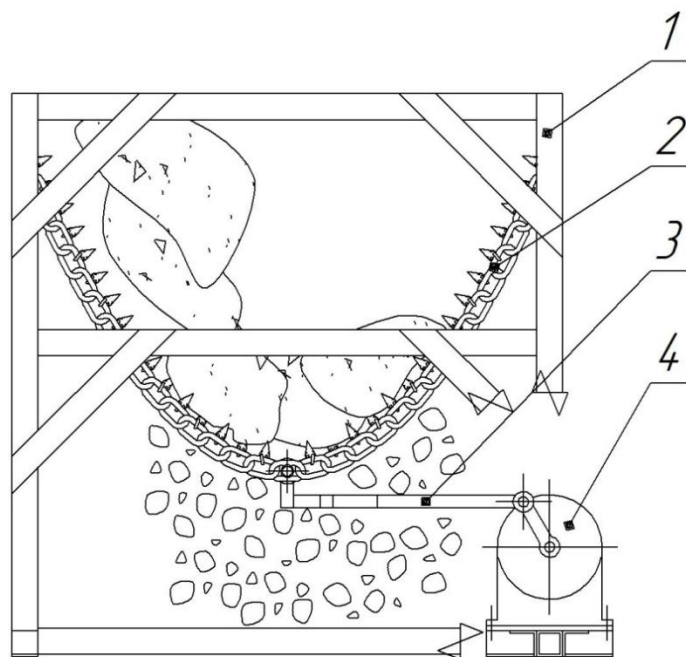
Рабочий привод цепного измельчителя: 1 – рама; 2 – рабочий орган; 3 – привод; 4 – кривошипно-шатунный механизм
